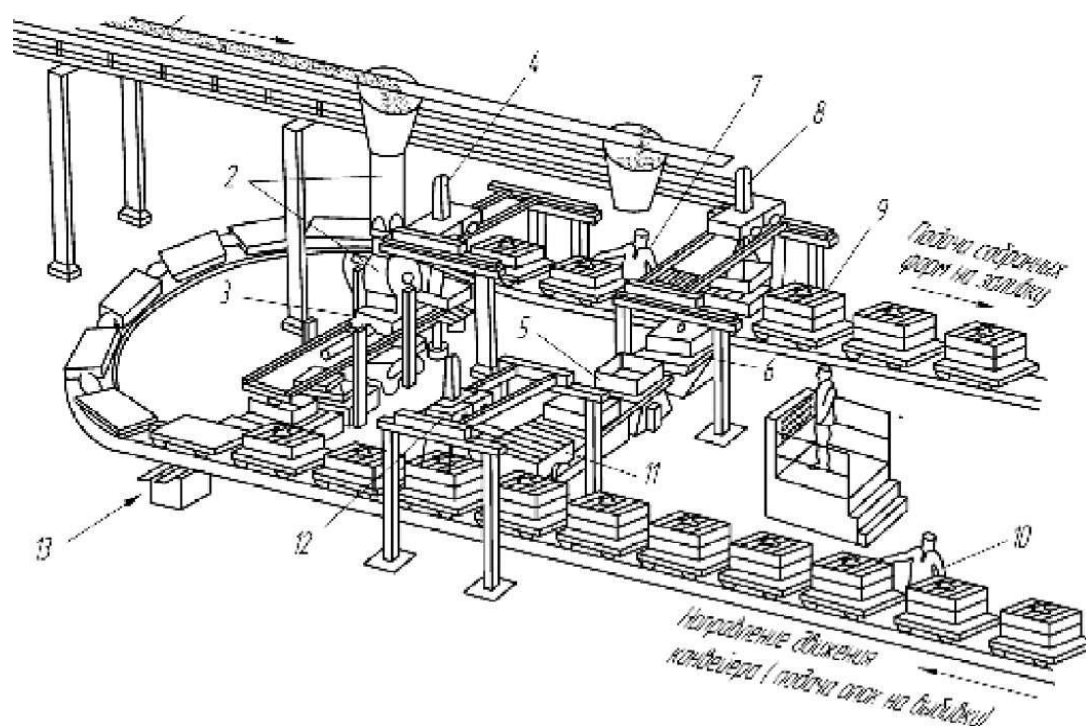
Автоматическая формовочная линия: 1 -транспортерная лента; 2 - бункер с дозатором; 3 -формовочный автомат нижних опок; 4 - механизм кан-тователя и подаватель нижних опок; 5 -формовочный автомат верхних опок; 6 -линия верхних опок; 7 -установка стержней; 8 -механизм сборки форм; 9 -заливочный конвейер; 10 -удаление splесков металла; 11 -автоматическая выбивная установка; 12 -механизм съема и распаровки опок; 13 -линия нижних опок
